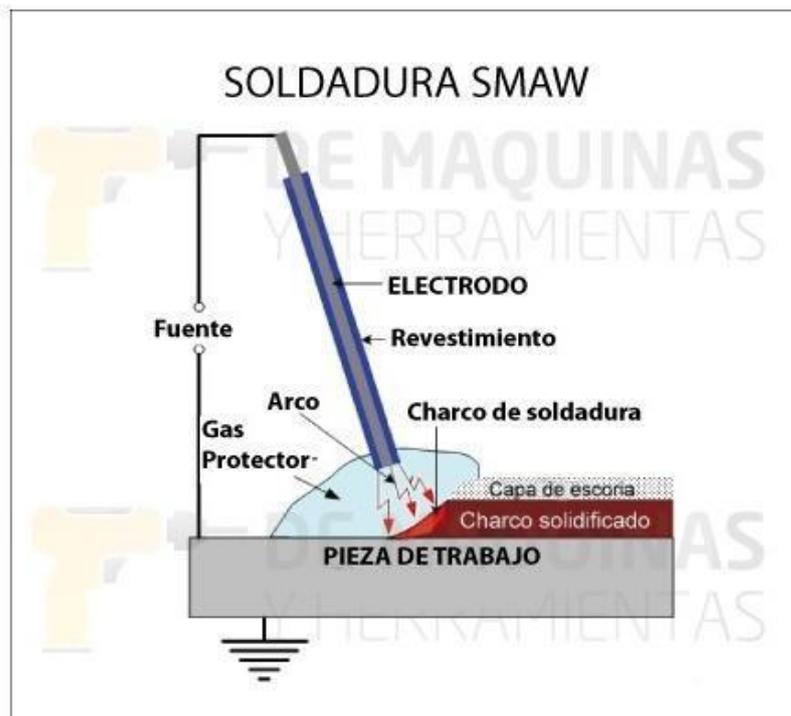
Soldadura con varillas como material de aporte proceso SMAW.
